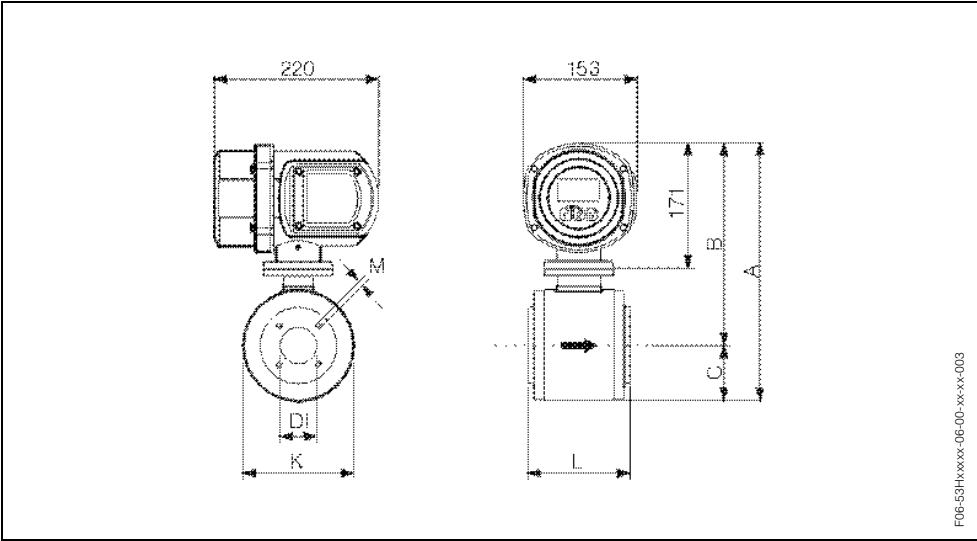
Dimensiones del Promag H / DN 40...100 (versión compacta, cabezal de acero inox. para montaje en campo)
